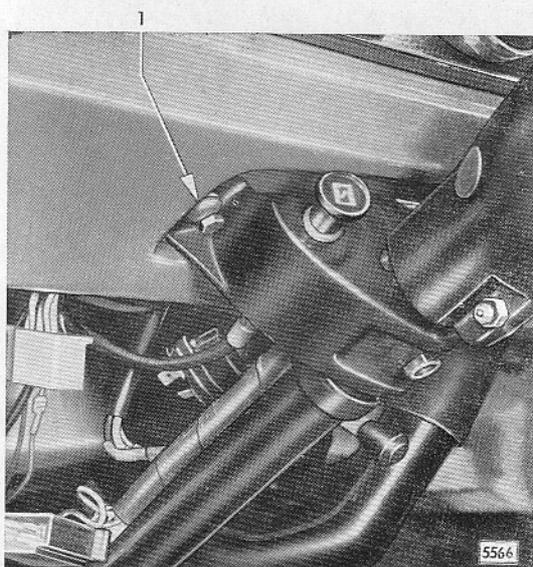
Abreißschrauben für Lenkstützrohr-befestigung lose eingeschraubt
